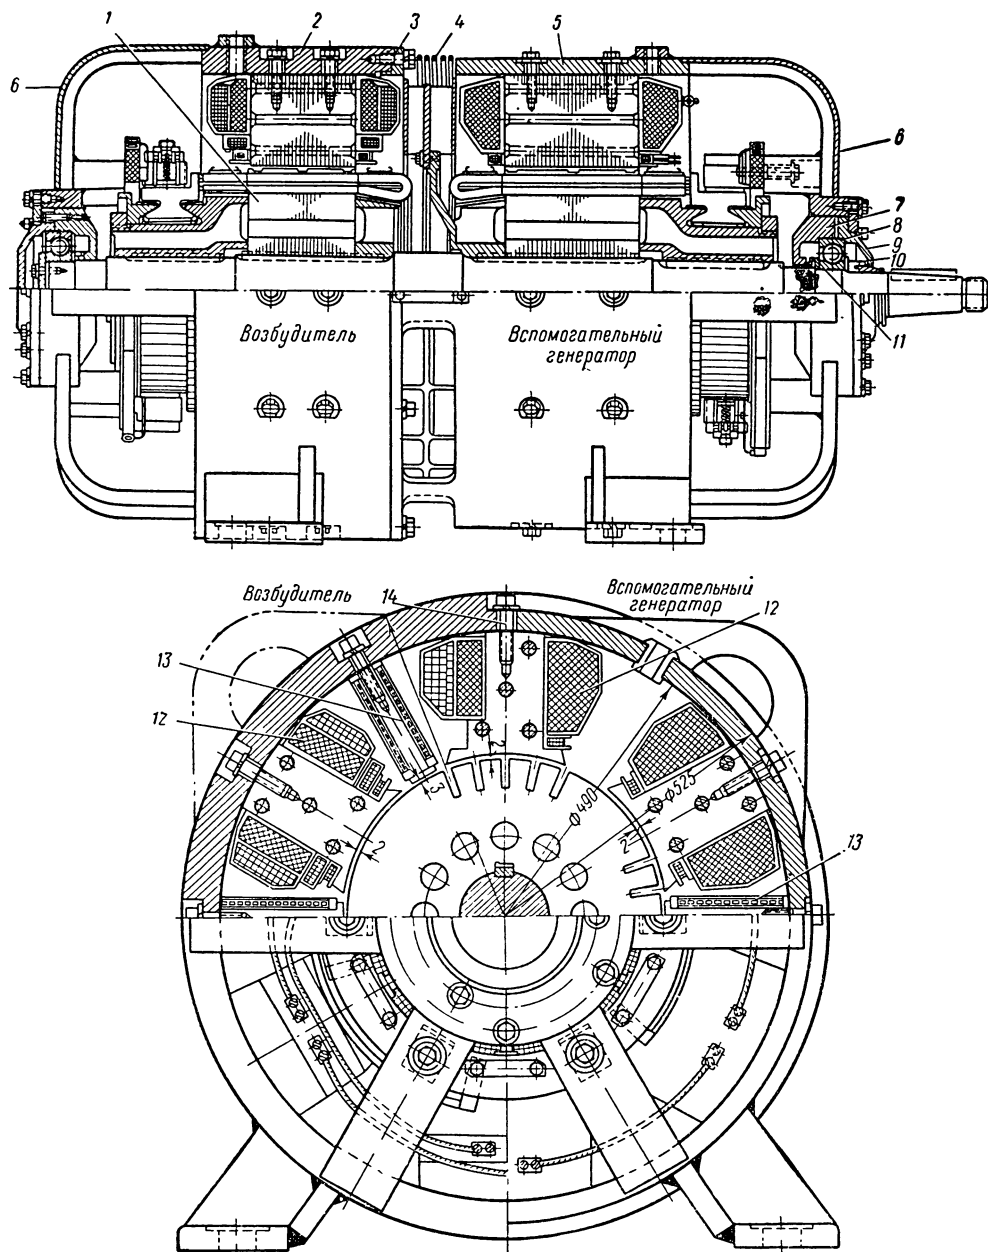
Двухмашинный агрегат ВТ275/120+ВГТ75/150:
